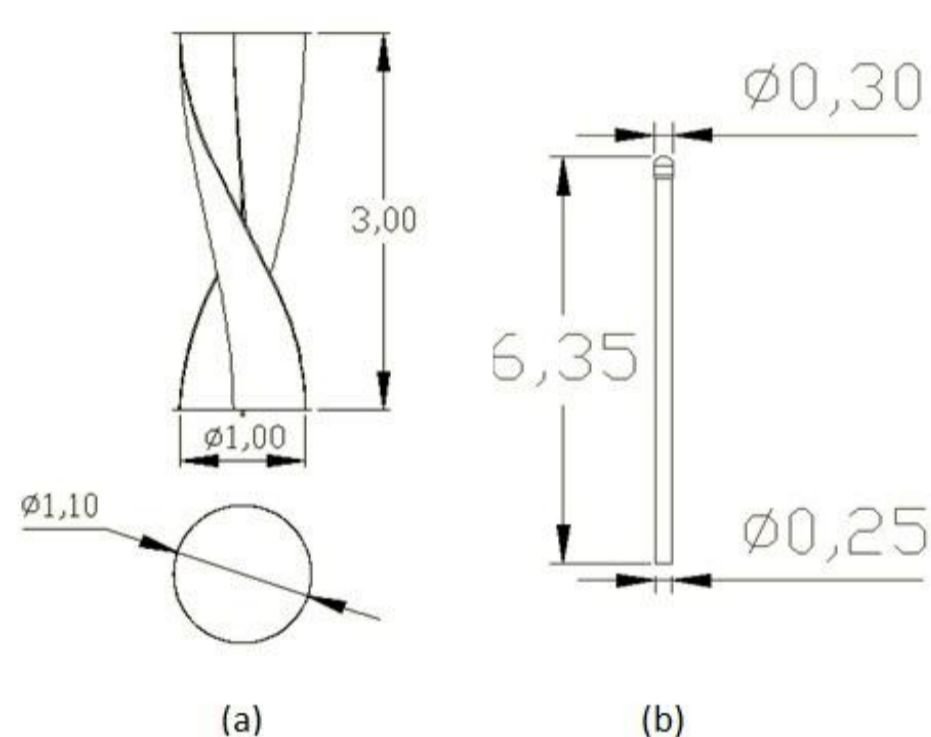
Geometria e dimensões, em metros, do rotor e da torre de fixação.
